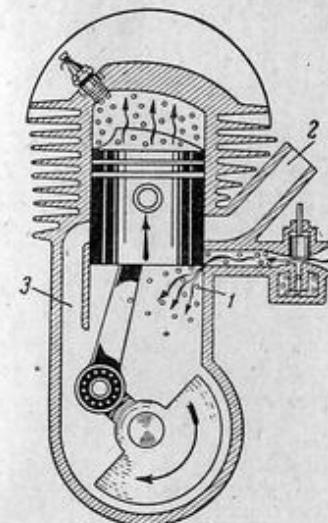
Двухтактный двигатель — поршень идет вверх:
